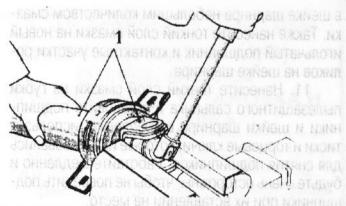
Надежно закрепите скобу центрального подшипника и карданный вал в тисках, отверните гайку центрального крепления
